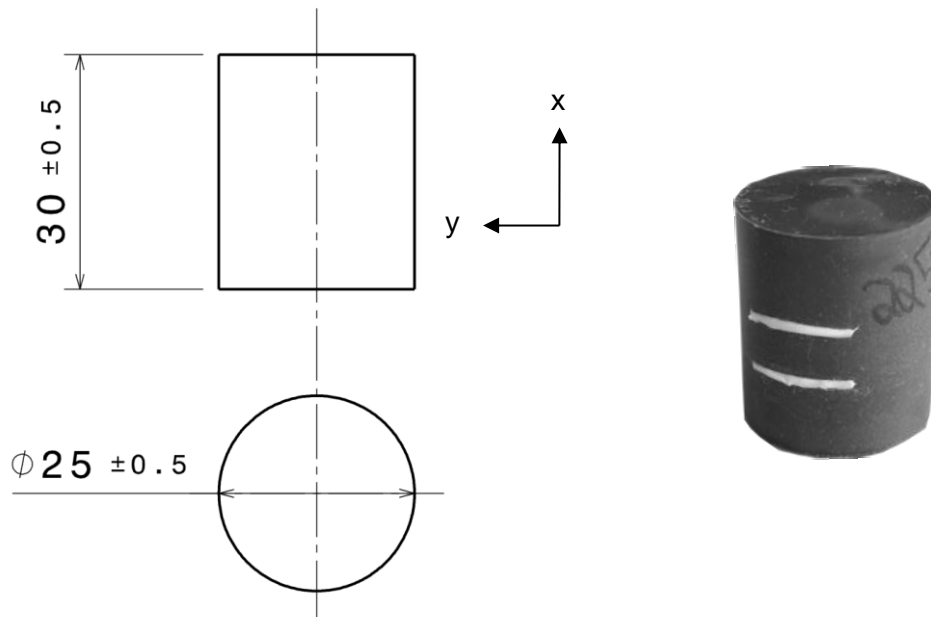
Druckprobe in Anlehnung an DIN EN ISO 604 und DIN ISO 7743 [88, 89] (technische Zeichnung links; Bild rechts)
